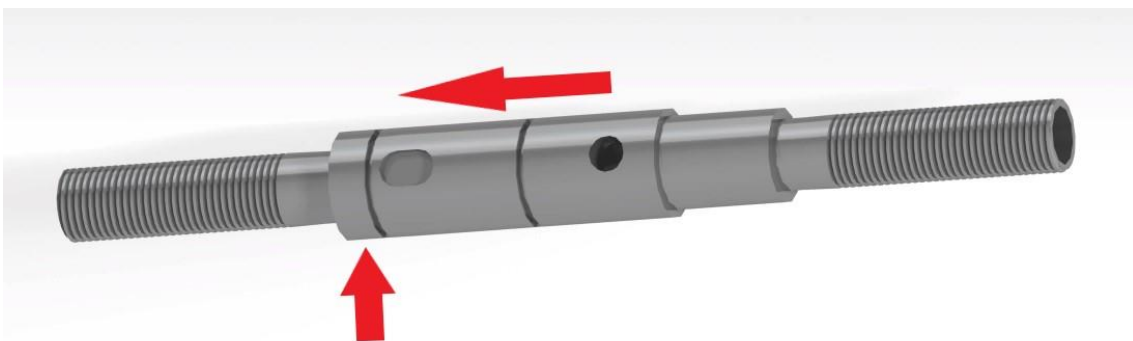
Vista en detalle del CILINDRADO_ACABADO_3 del eje (Fuente: elaboración propia)
